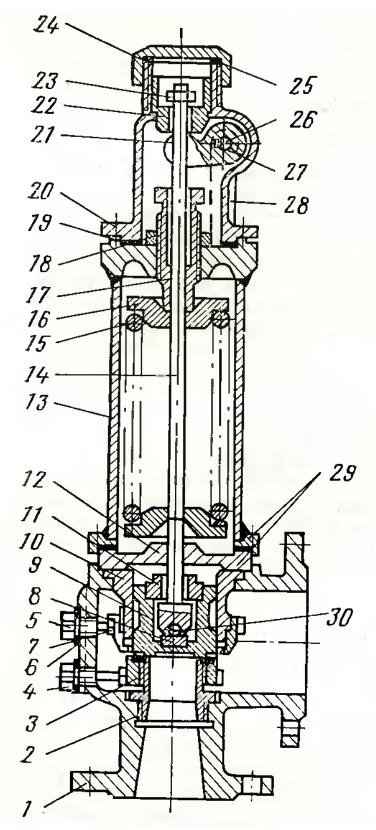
Пружинный предохранительный клапан типа ППК 1 - корпус; 2 -сопла; 3 - нижняя регулировочная втулка; 4, 5 - стопорный винт; 6, 19, 25, 29 -
